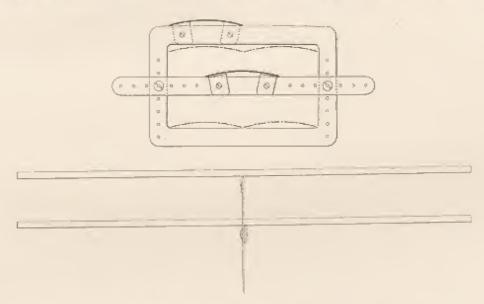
Montage des hiplans : vue de profil et vue de tuce.
